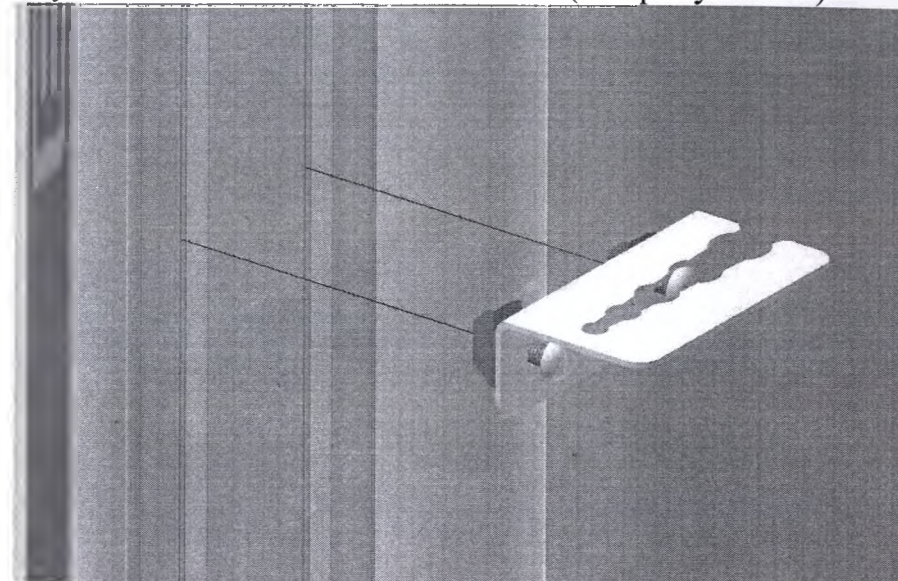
Установка держателя трубок присоединённых к банкам для сбора жидкости
